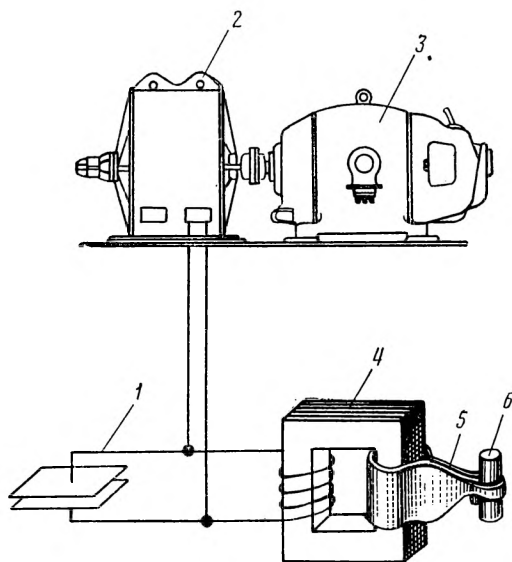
Схема установки для нагрева изделий токами высокой частоты
